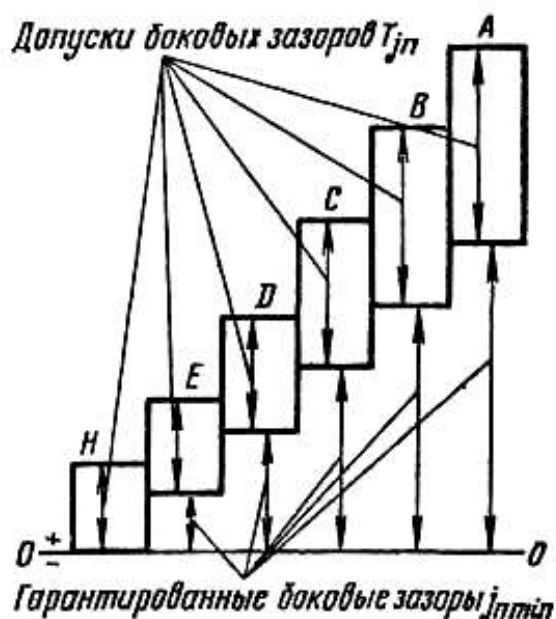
Схема расположения полей допусков боковых зазоров (T_{jn}) для принятых видов сопряжений зубьев зубчатых колес
